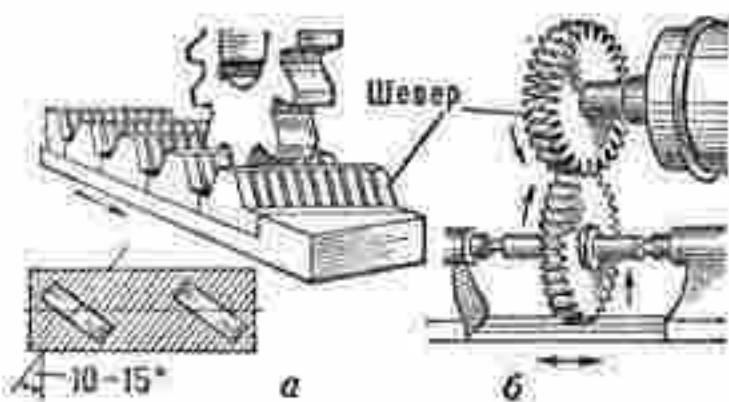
Схемы шевингования цилиндрических зубчатых колес: а — реечным шевером; б — дисковым шевером.
